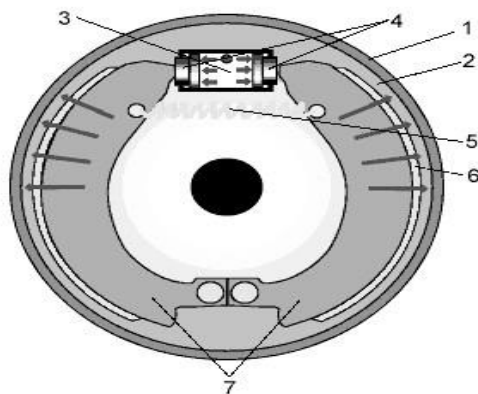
Схема работы барабанного тормозного механизма: 1 - тормозной барабан; 2 - тормозной щит; 3 - рабочий тормозной цилиндр; 4 - поршни рабочего тормозного цилиндра; 5 - стяжная пружина; 6 - фрикционные накладки; 7 - тормозные колодки.
